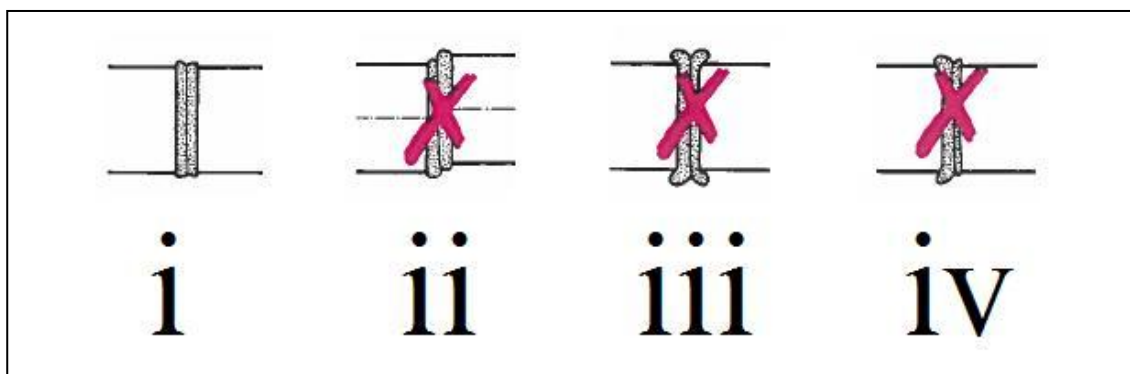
Verificação visual da eletrossoldadura. i - Correto; ii - Desalinhamento; iii - Demasiada pressão no início da soldadura; iv - Aquecimento desigual nos dois tubos[22]
